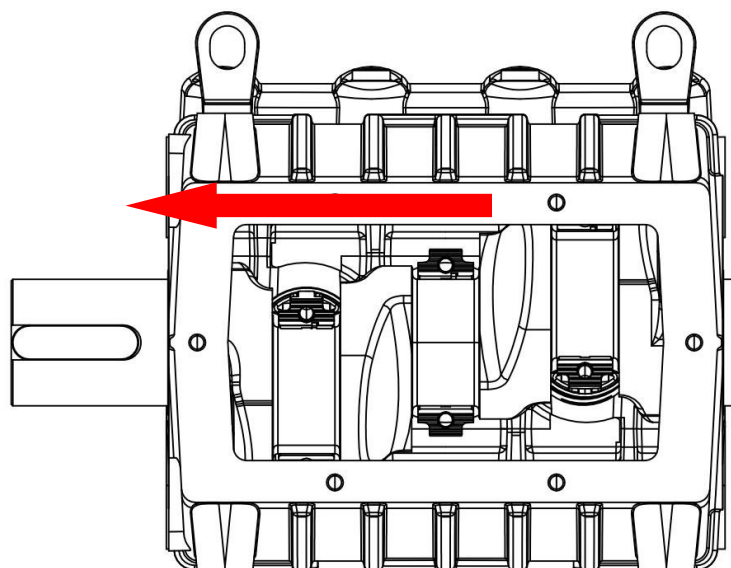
Коленчатый вал и шатуны в картере (вид со стороны задней крышки)
